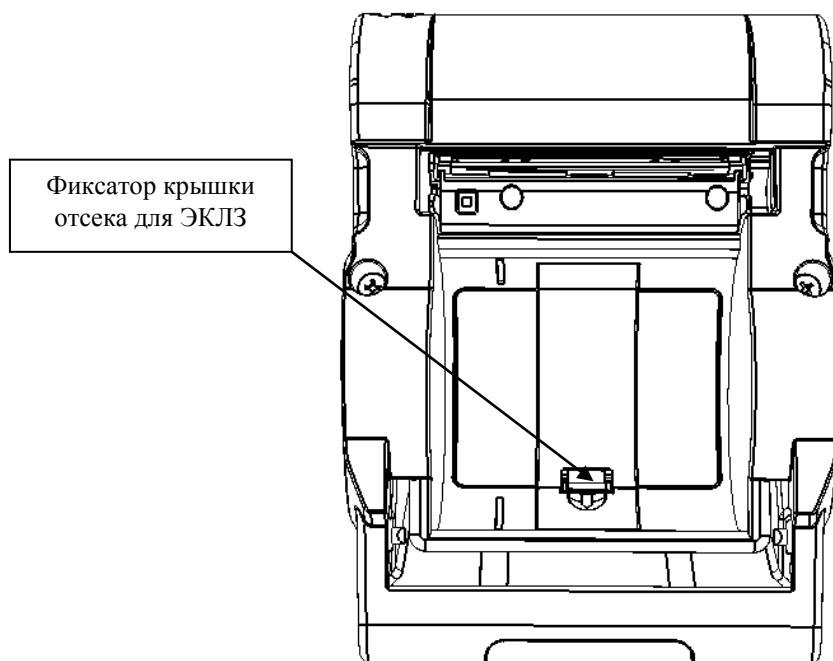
Расположение фиксатора крышки отсека для ЭКЛЗ
